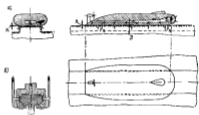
Схема машины четвертого типа: а — вход на воздушной смазки; б — выход воздуха на воздушной смазки и рельс.
